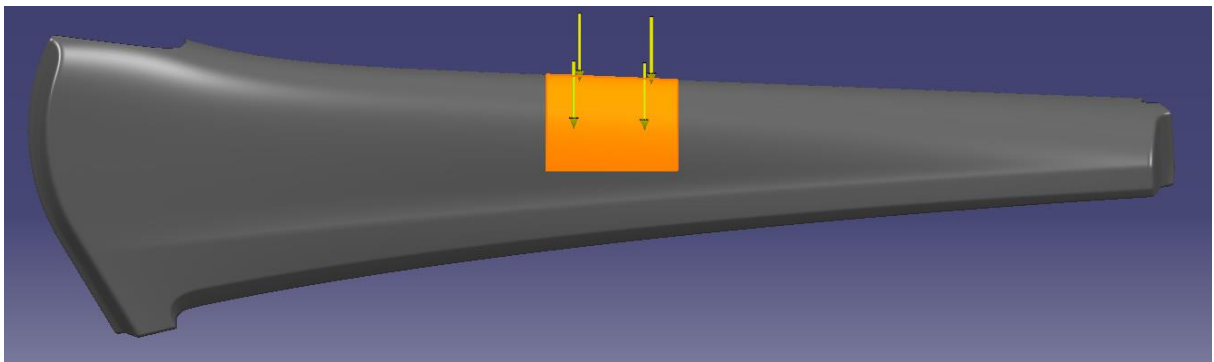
Zona de aplicación de la fuerza (vista frontal)
